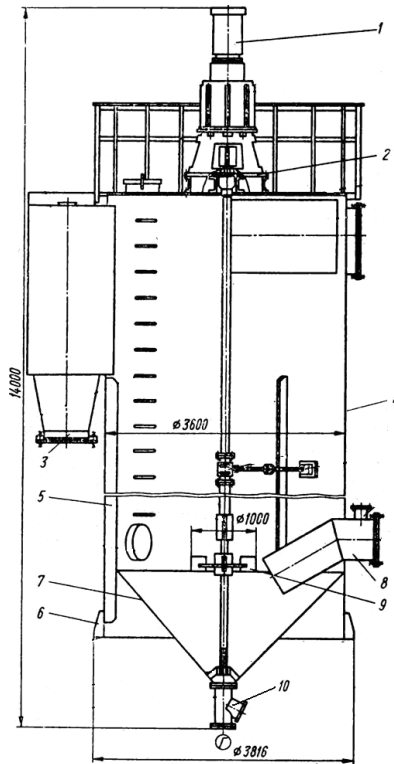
Дефекатор ОД-6: 1 – привід; 2 – рама; 3 – короб; 4 – корпус; 5 – контролювальна панель; 6 – опора; 7 – конічне дно; 8 – патрубок для підводу соку; 9 – лопатева мішалка; 10 – кутовий вентиль.
